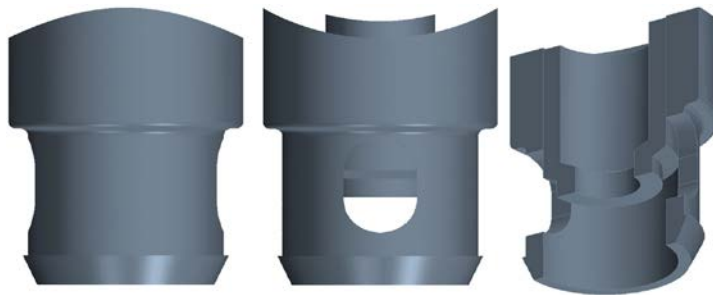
Конструкции форсунок для их установки в продувочную трубу
